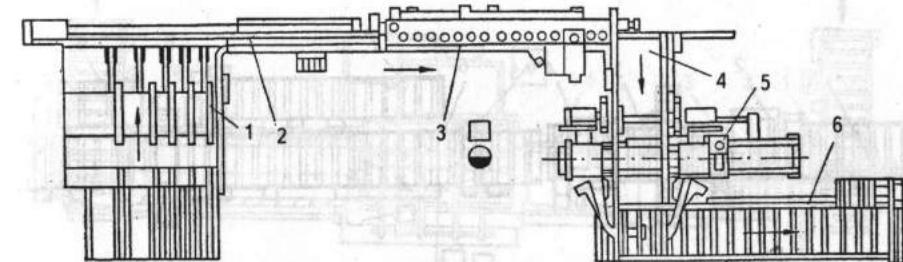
Лінія для поздовжнього фрезерування брусків і зарізування шипів АЛБ-1:
